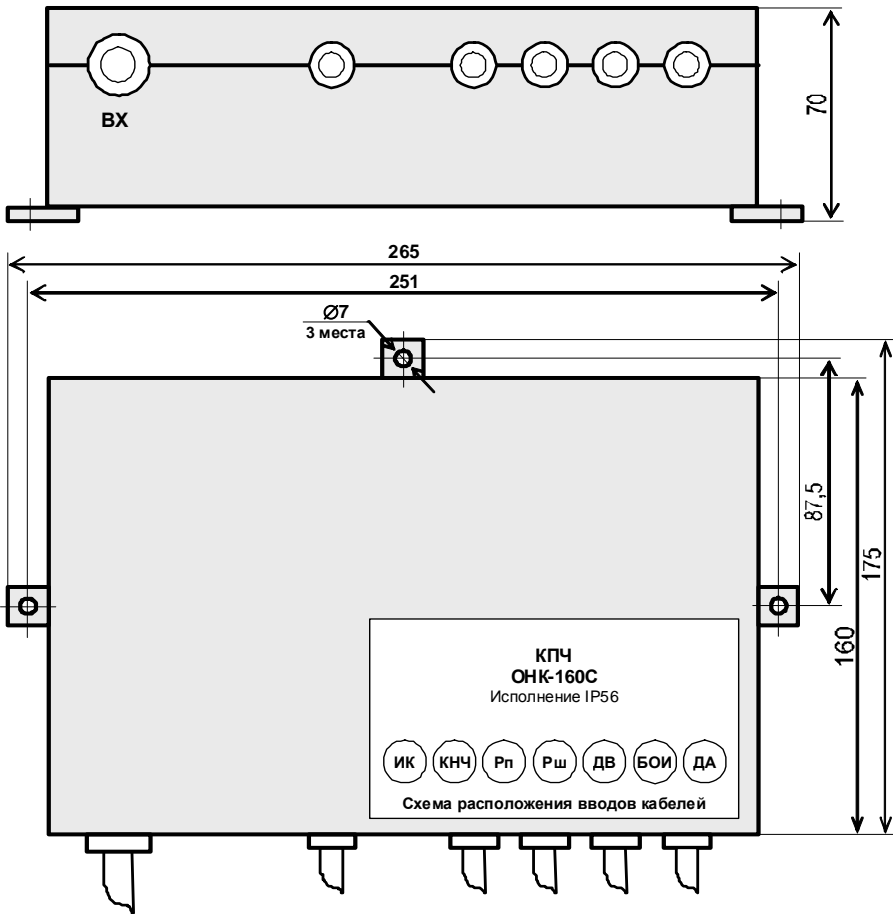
Габаритные и присоединительные размеры КПЧ
